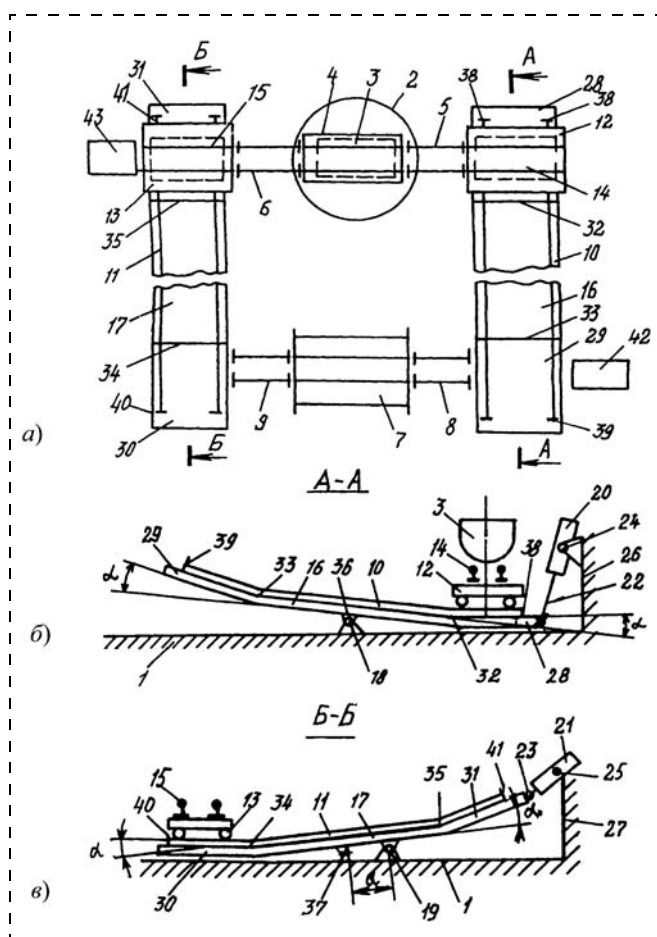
Приемная площадка надшахтного здания по первому варианту: а — план перекрытия с расположением оборудования, соответствующим моменту, предшествующему выкатыванию грузной вагонетки из клетки; б — разрез А-А при расположении рамы с первым дополнительным рельсовым путем в момент приема грузной вагонетки на платформу; в — разрез Б-Б при расположении рамы со вторым дополнительным рельсовым путем перед приемом порожней вагонетки с опрокидывателя
